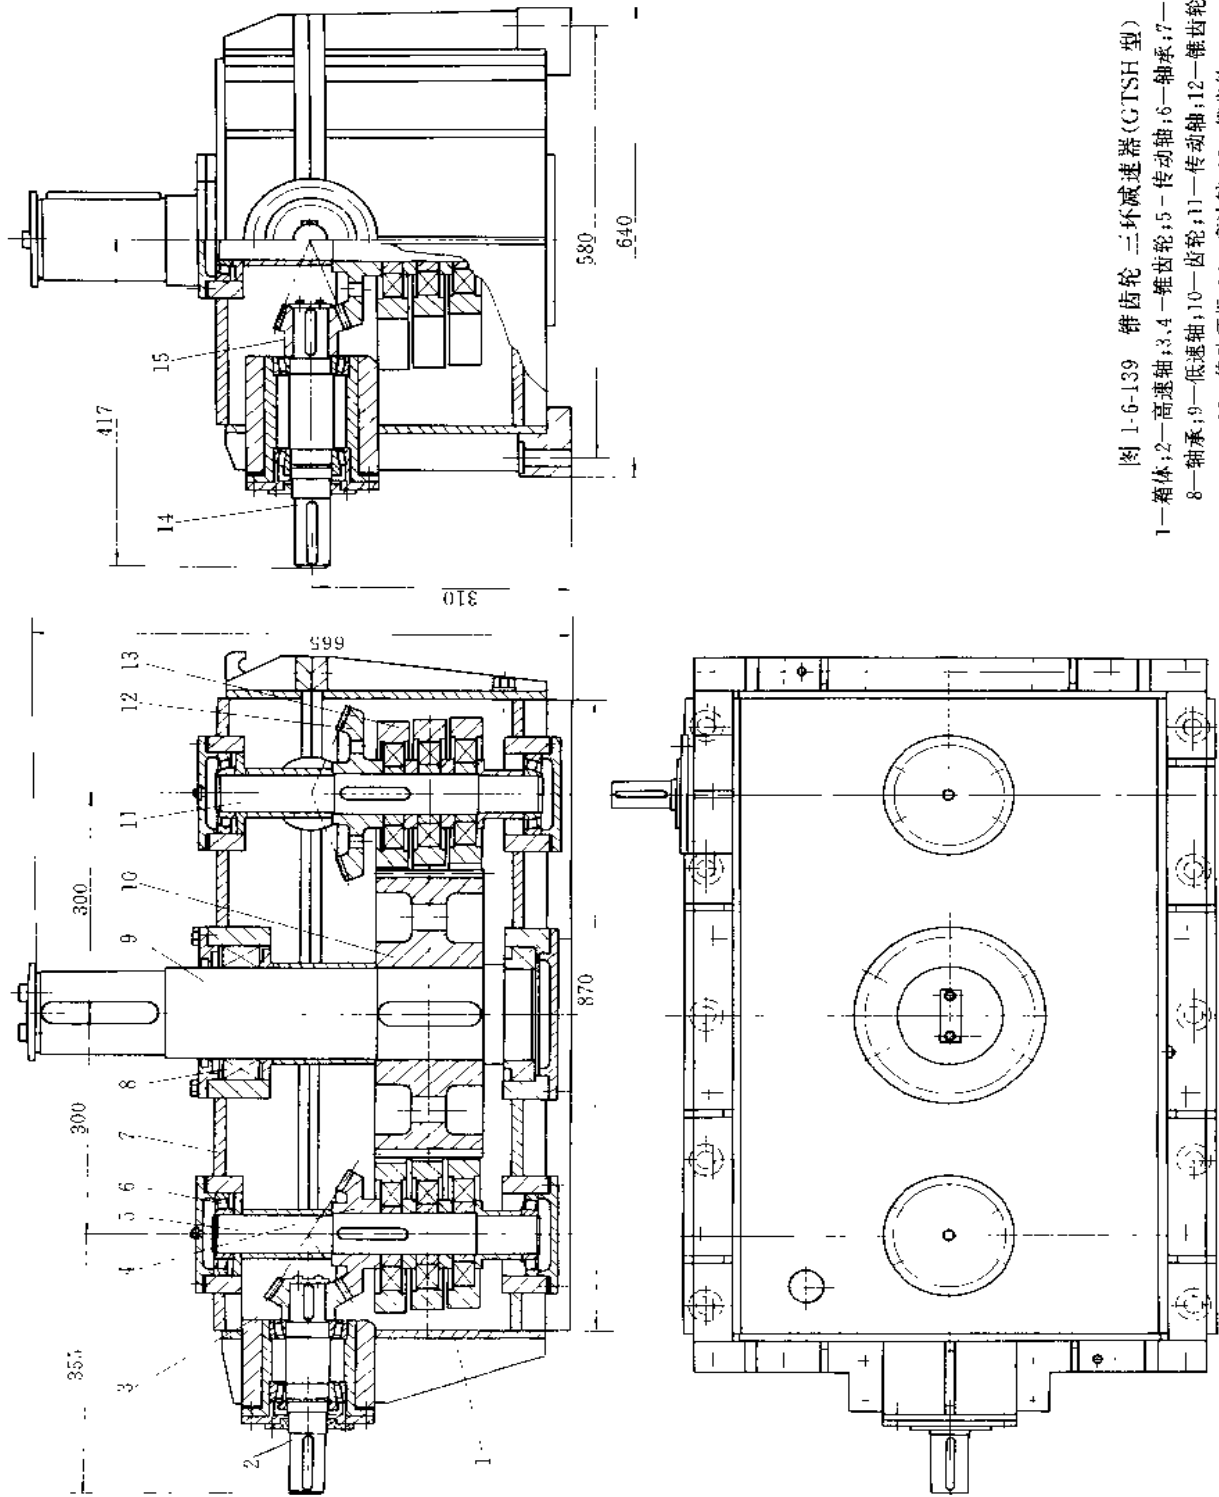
锥齿轮 三环减速器 (GTSH 型)
